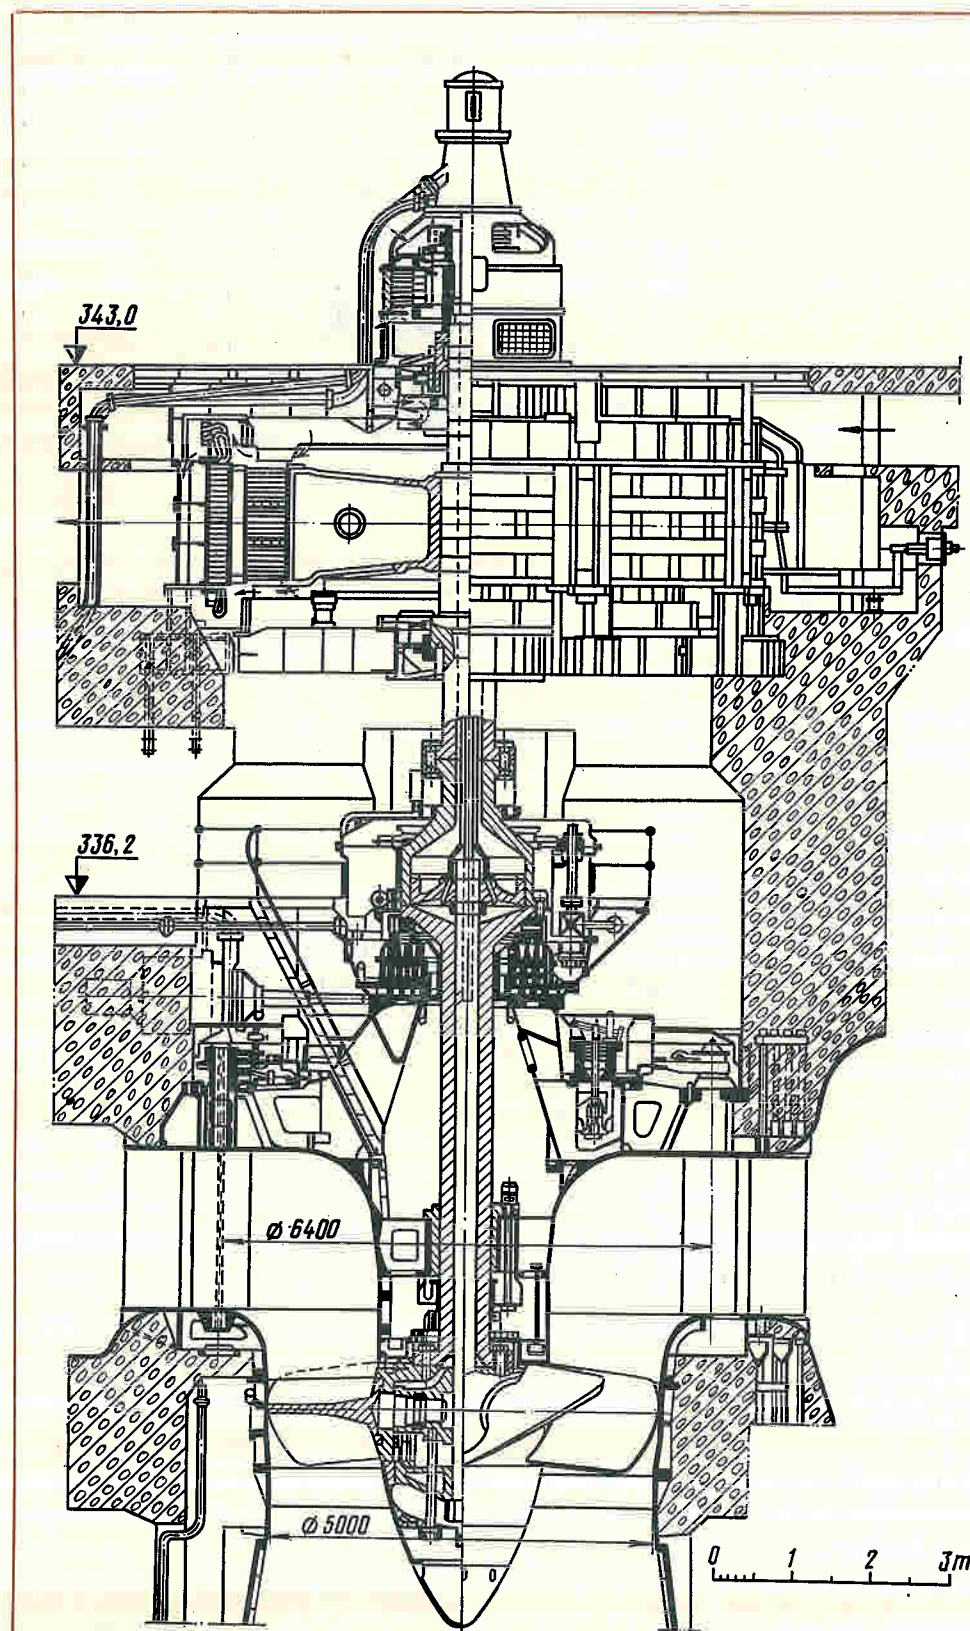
Вертикальный гидроагрегат с расположением сервомотора рабочего колеса во фланцевом соединении и подпятника на крышке турбины
